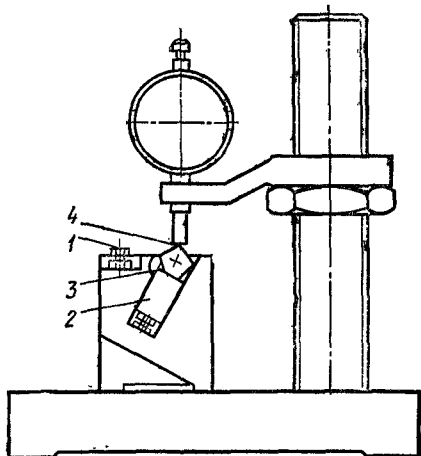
Схема приспособления для предварительной настройки на размер резцовых вставок
